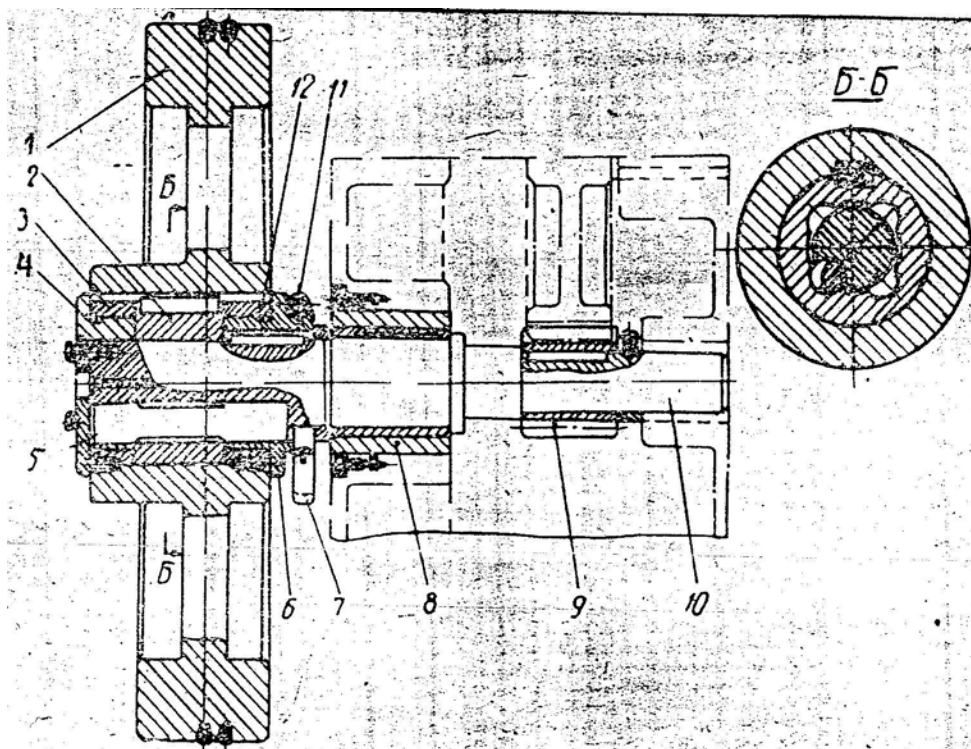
Конструкция привода ползуна с ножом и пуансоном
